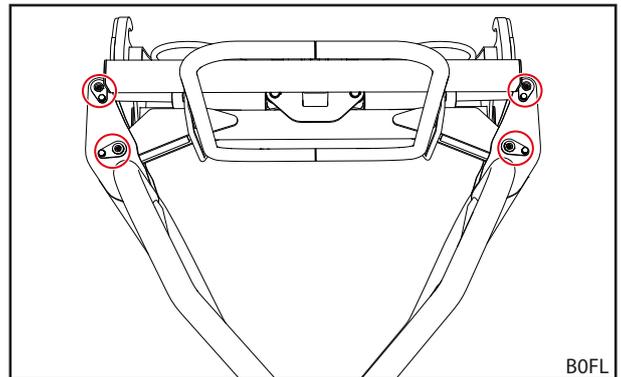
Puntos de engrase de la pinza para pacas encintadas
